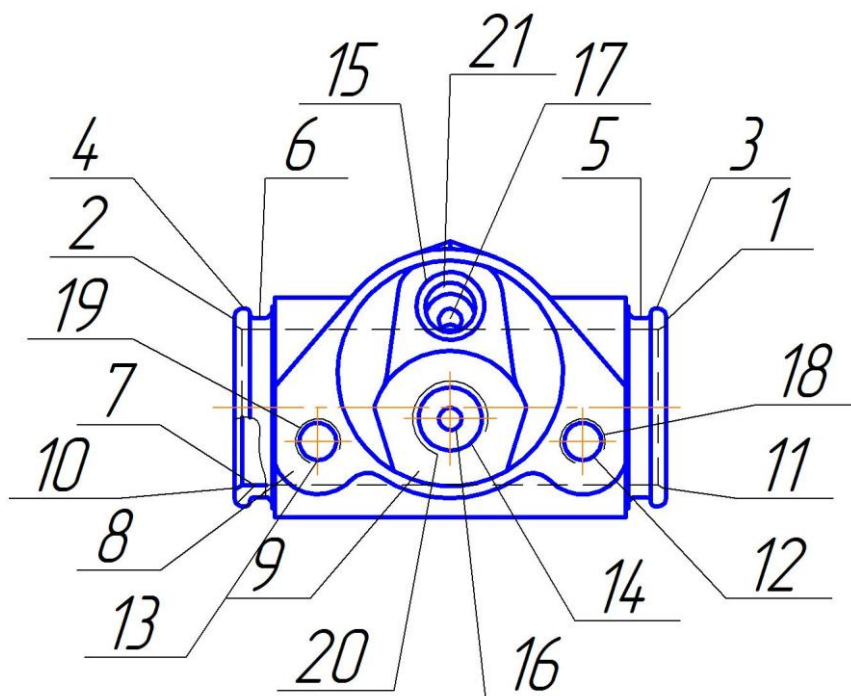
Обозначение обрабатываемых поверхностей.
